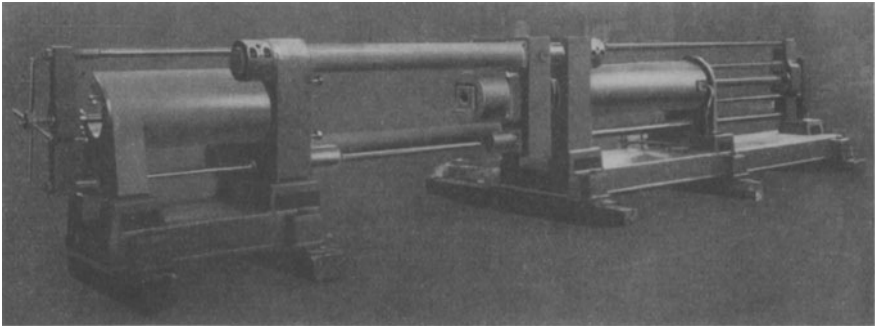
Einfachwirkende waagerechte Ziehpresse mit hydraulischem Stößelantrieb.
